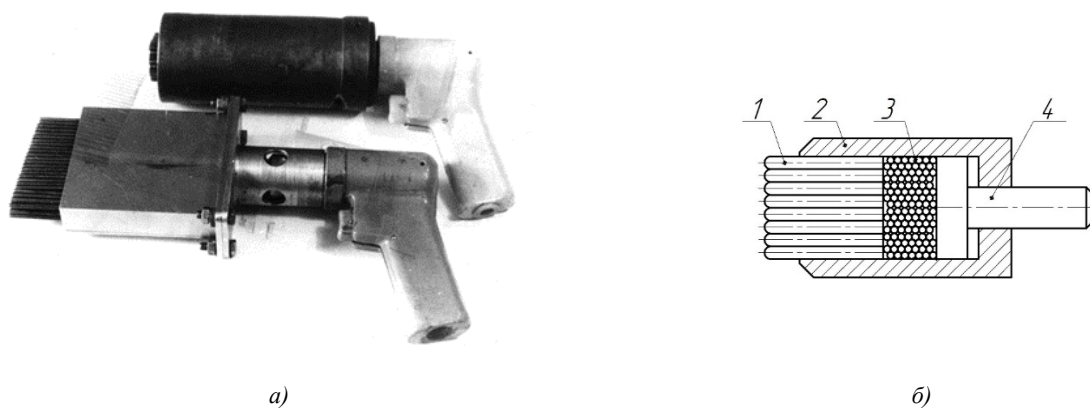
Внешний вид со схемой шарико-стержневого упрочнителя:
